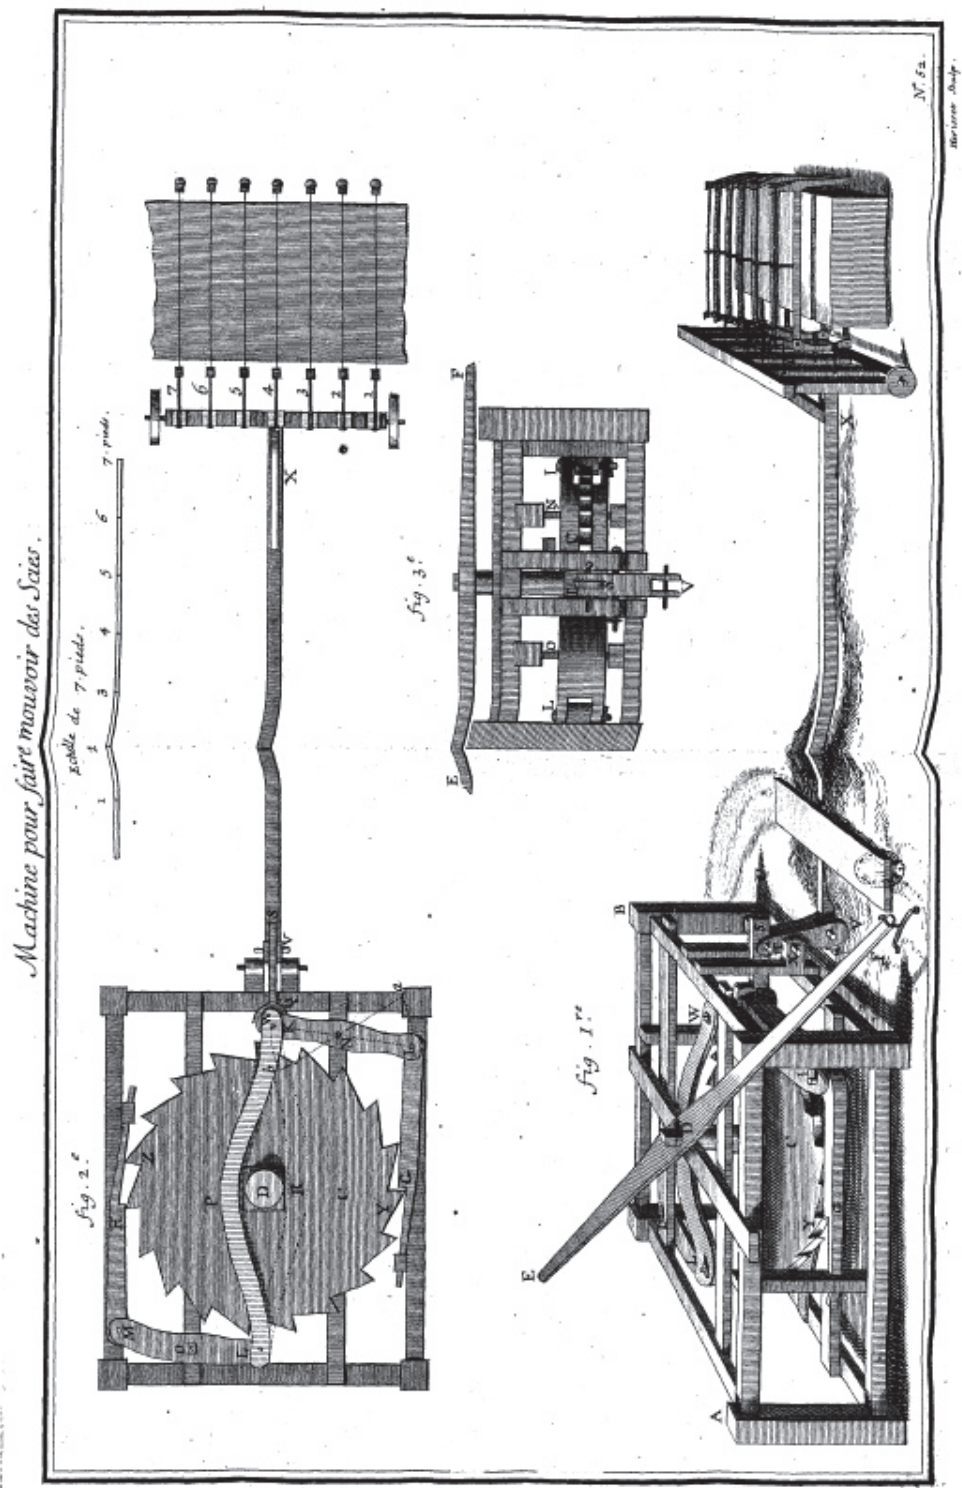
Machine pour faire mouvoir de six à sept scies, mue par les chevaux, approuvée en 1699 et figurant dans le tome I des Machines, p. 168.
